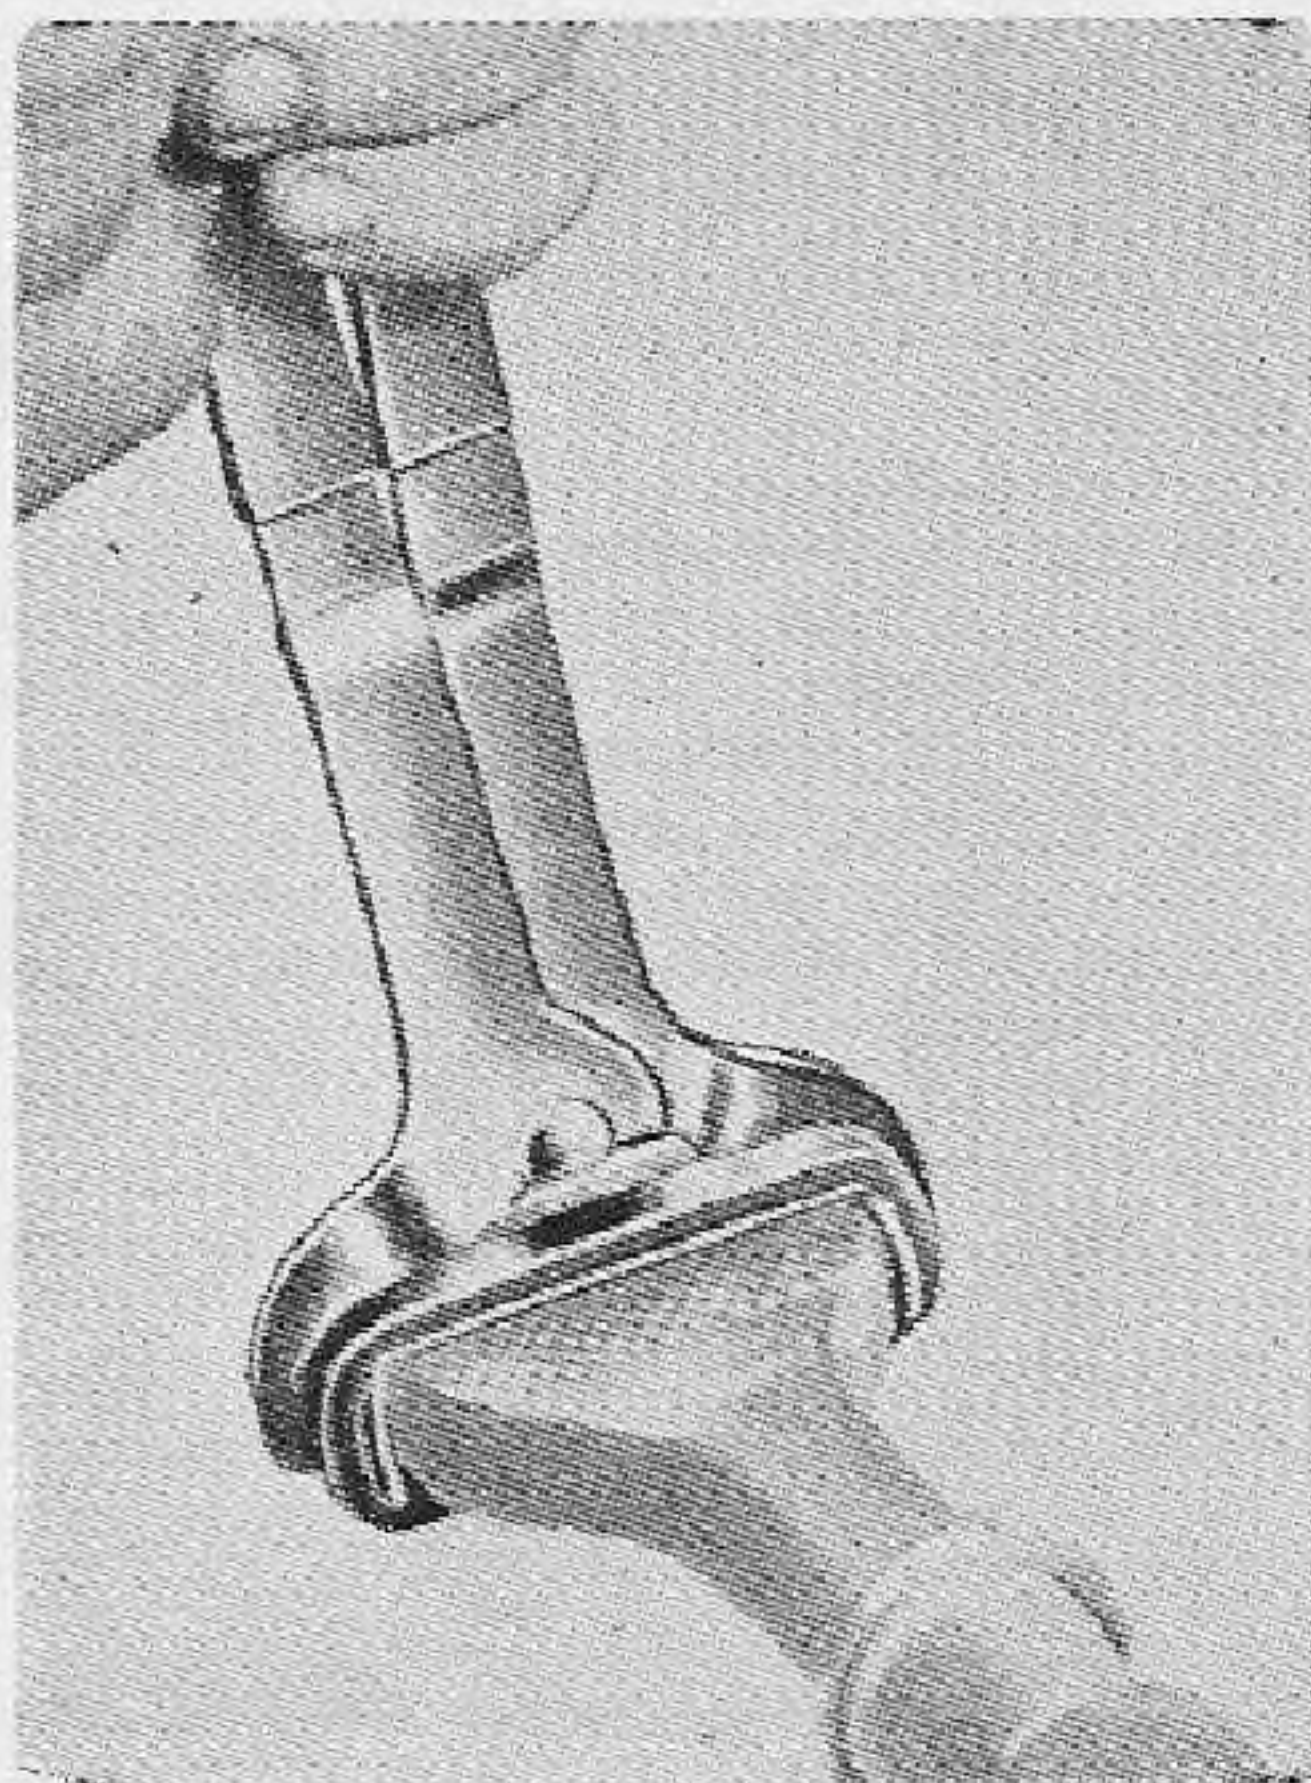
Montaje del anillo retén con la pinza DK 103.
